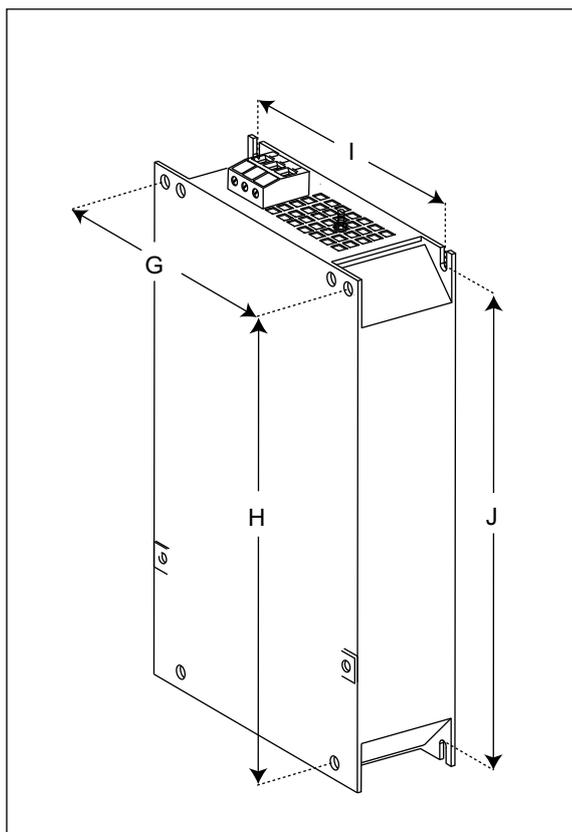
Quote di montaggio della bobina di rete, grandezze costruttive FSB e FSC
